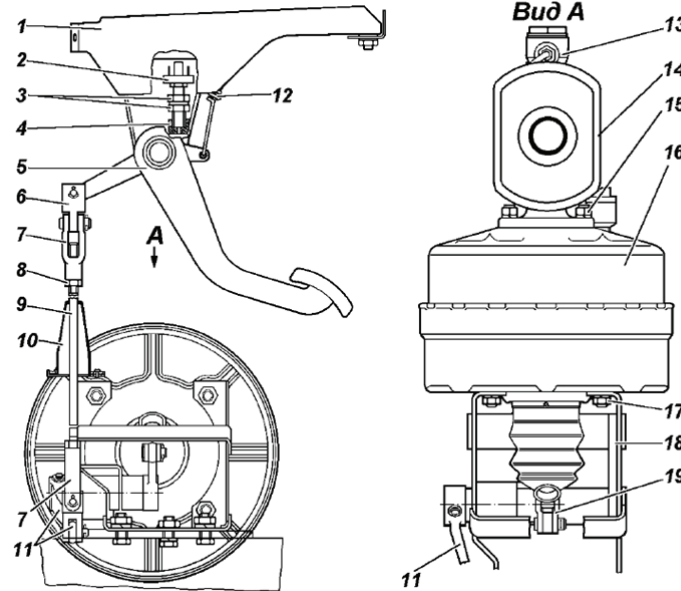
Привод главного тормозного цилиндра:
